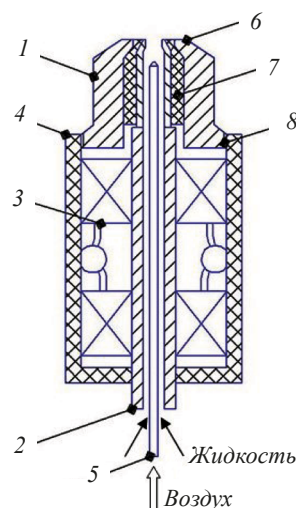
Форсунка для распыления суспензии для сушки пищевых порошков: 1 – неметаллическая трубка для подачи горячего воздуха; 2 – ферромагнитная трубка для подачи суспензии; 3 – встречно включенные соленоиды; 4 – немагнитный корпус; 5 – сопло; 6 – форсунка; 7 – демпфирующий элемент; 8 – резьбовое соединение
